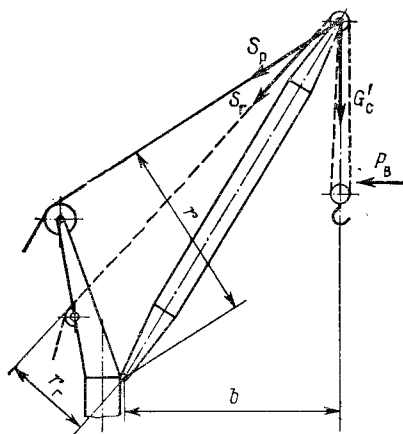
Схема к расчету устойчивости стрелы башенного крана против опрокидывания назад
